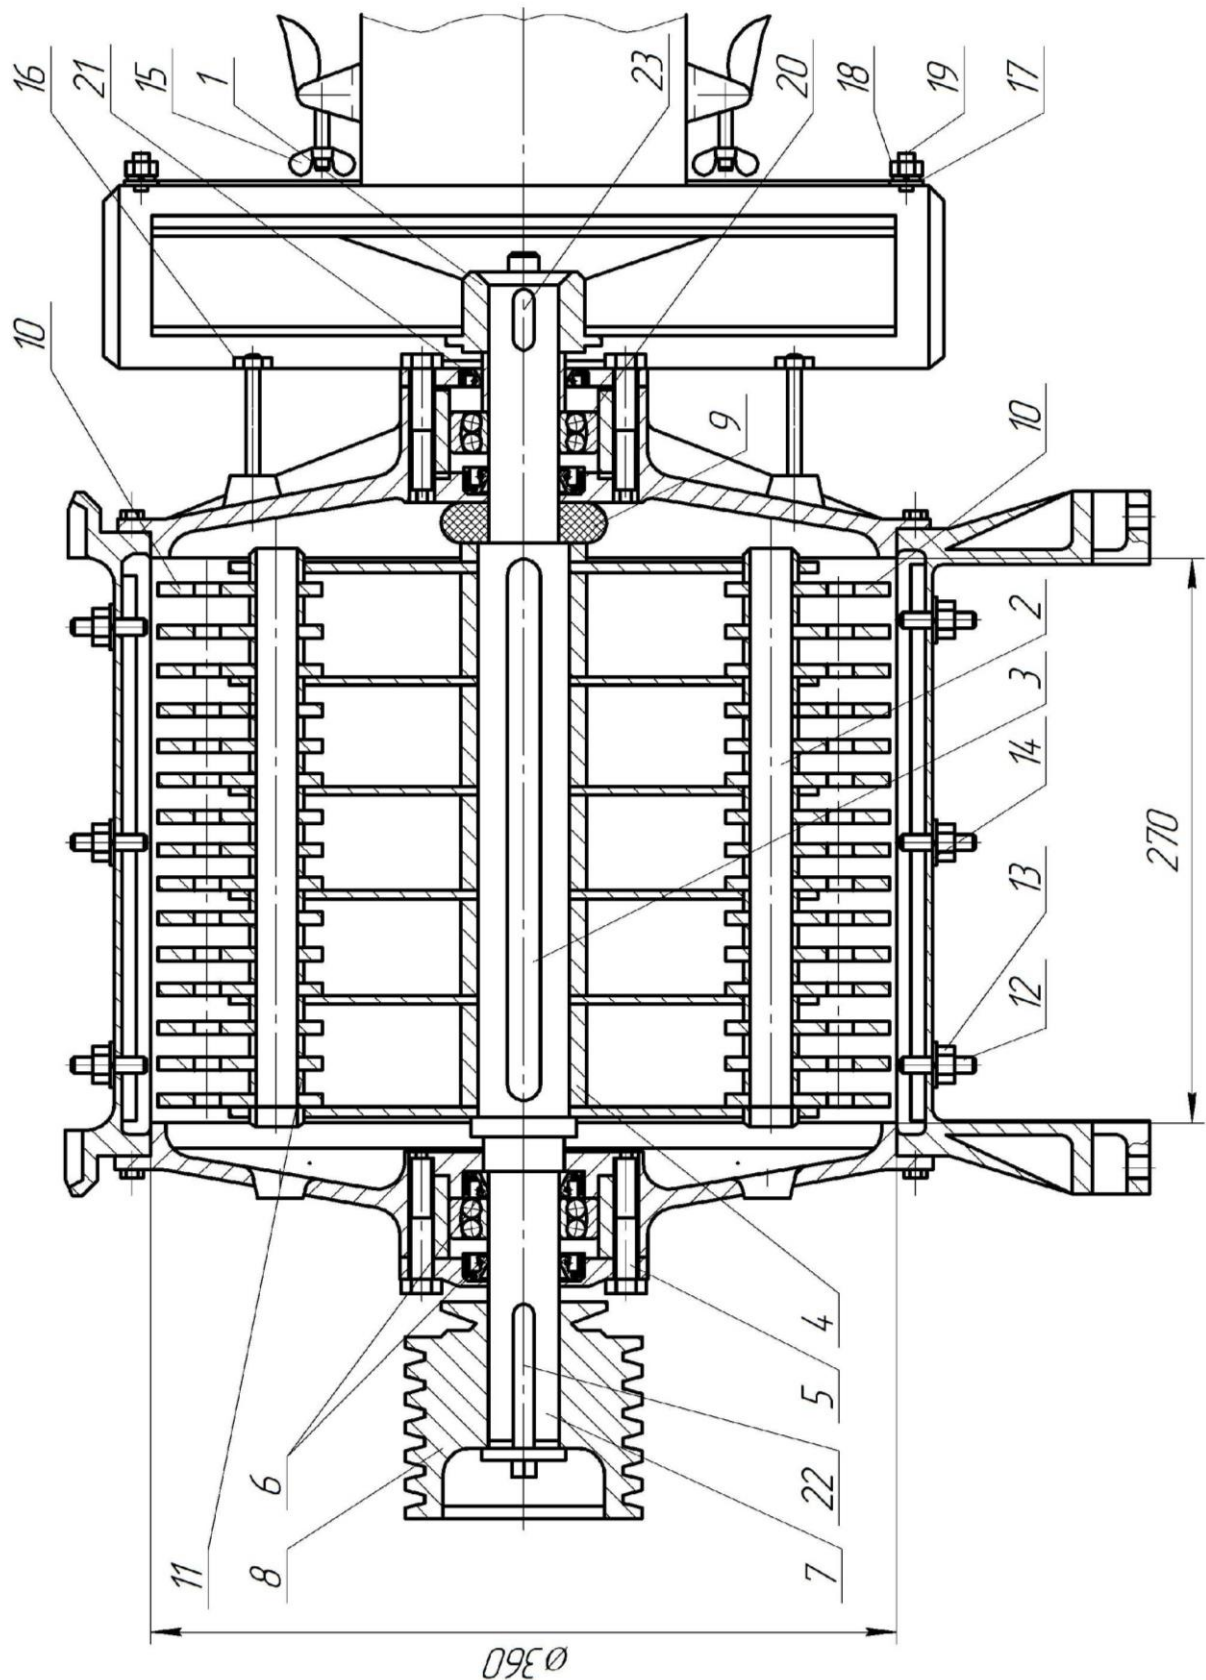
Подрібнювальний апарат кормодробарки:
